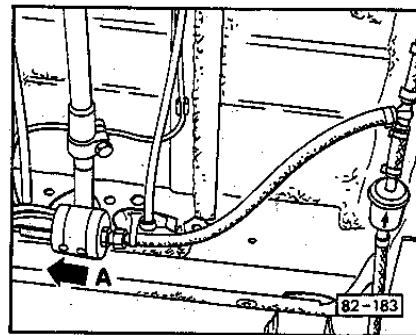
Kraftstoffpumpe prüfen/einstellen, eingebaut
